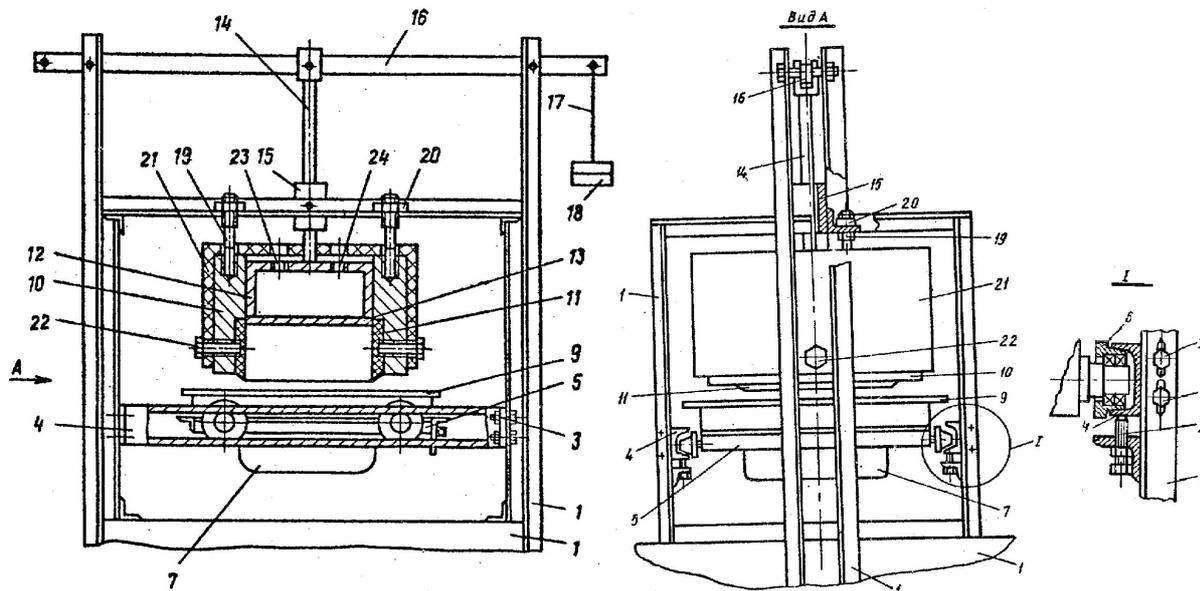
Сдвиговой стенд (разрез, вид спереди, увеличенный вид ролика)
